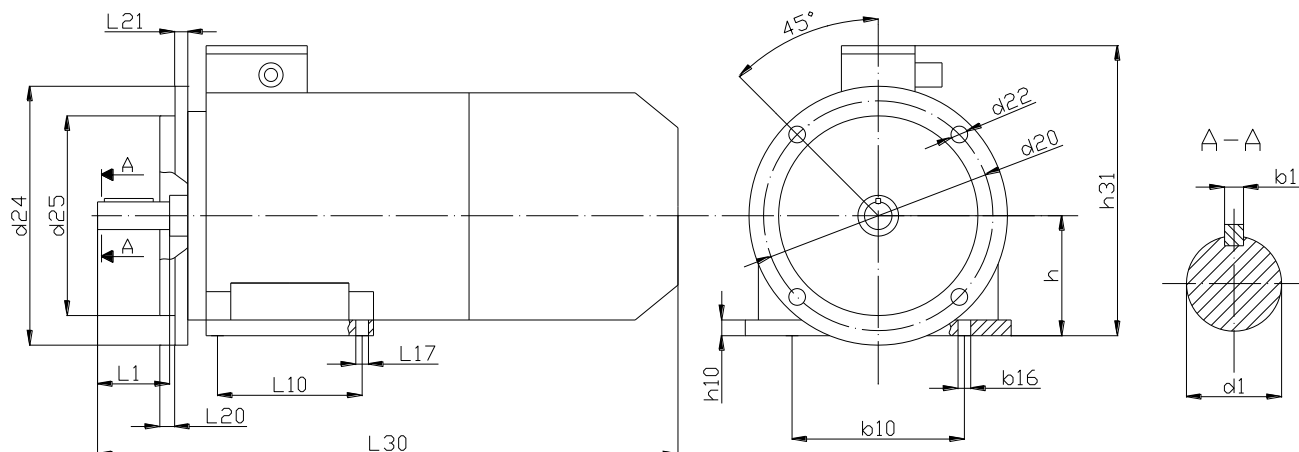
Габаритные и установочно-присоединительные размеры
